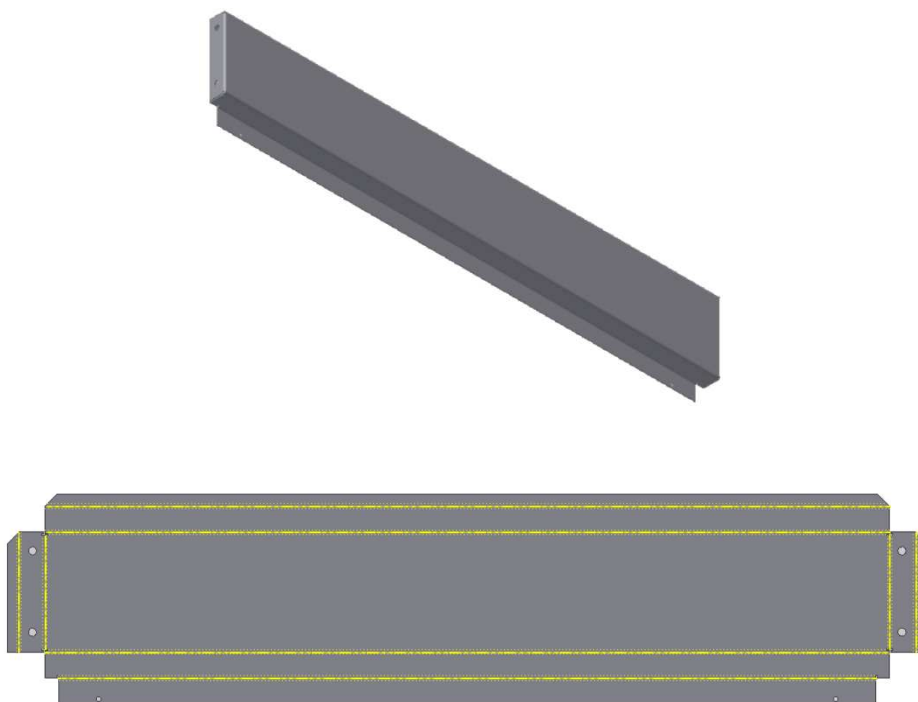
Isométrica y Desarrollo del dintel frontal.
